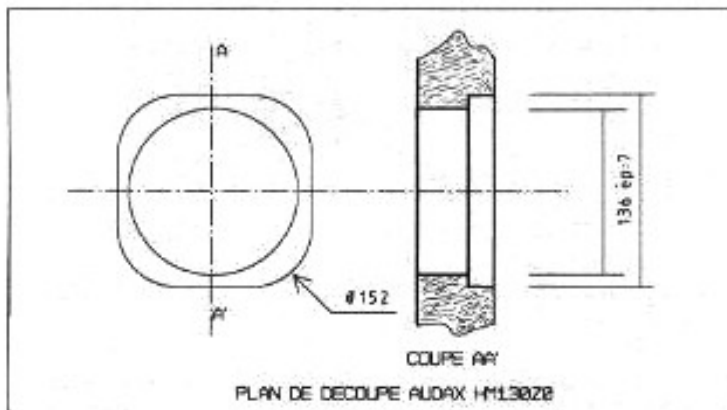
Plan de découpe de la façade avant pour le médium Audax HM 130 20.
